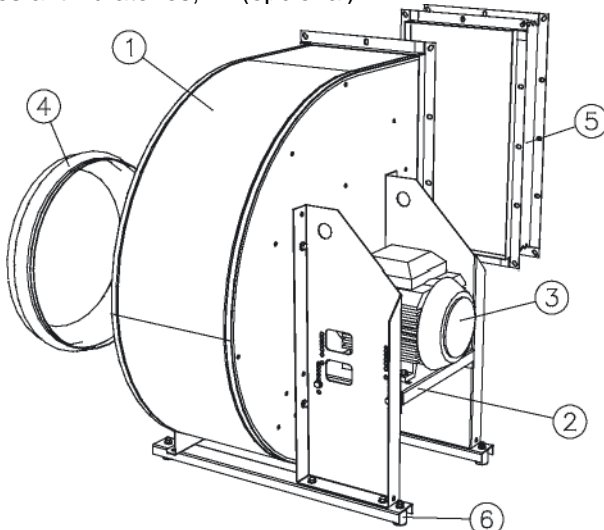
Elementos de montaje del ventilador CXRT.
